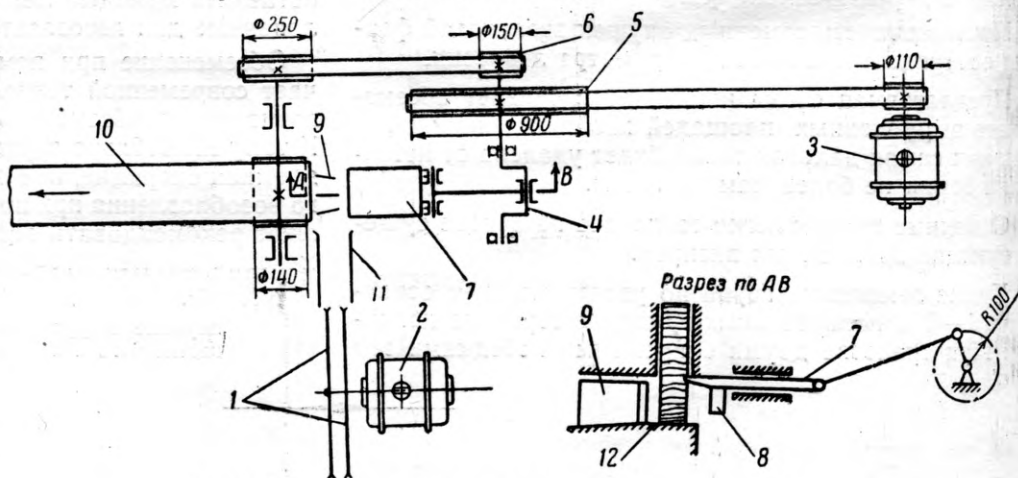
Кинематическая схема пильно-кольного агрегата:
